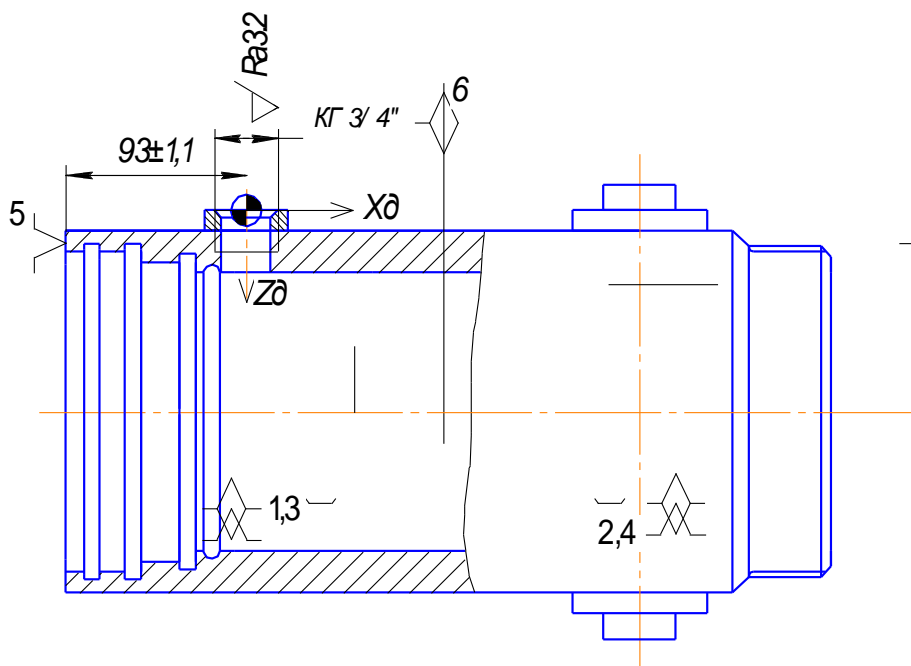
Схема базування заготовки на операції свердлильній з
